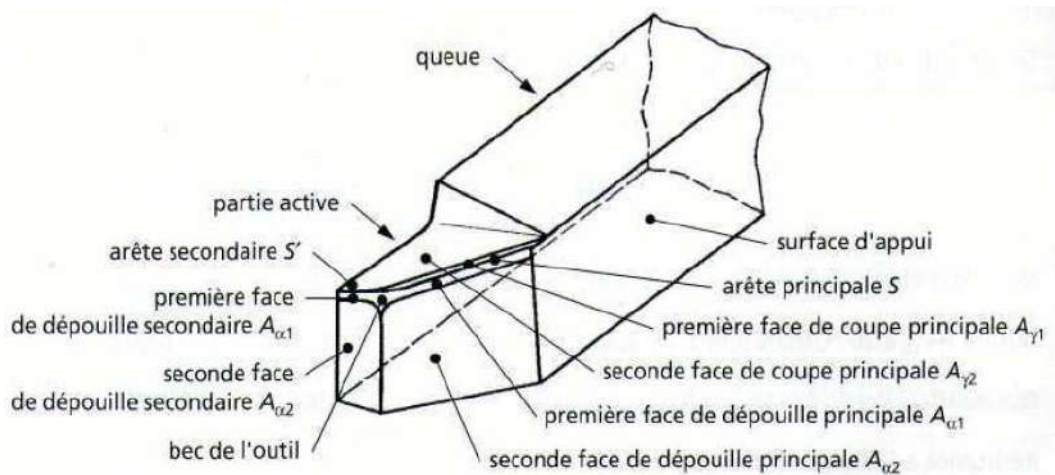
Faces et arêtes d'un outil de tournage [3].
